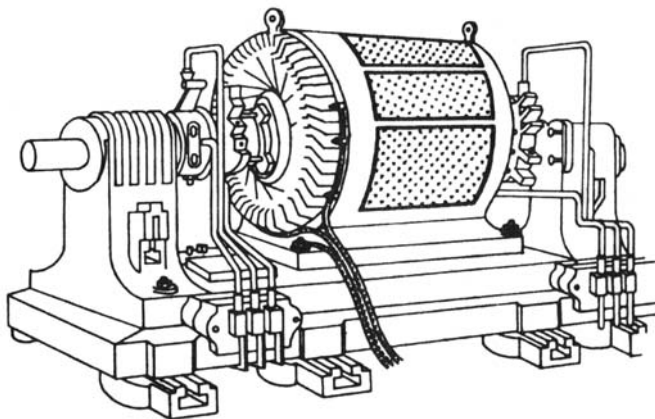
Общий вид двигателя Доливо-Добровольского
